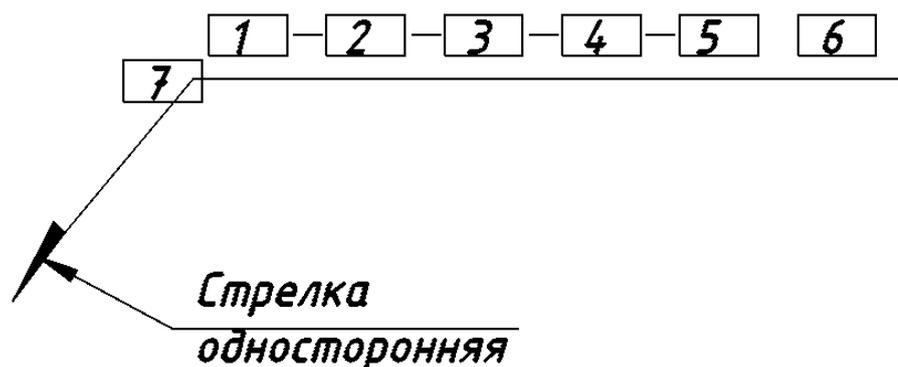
Образец выполнения условного обозначения сварного шва
